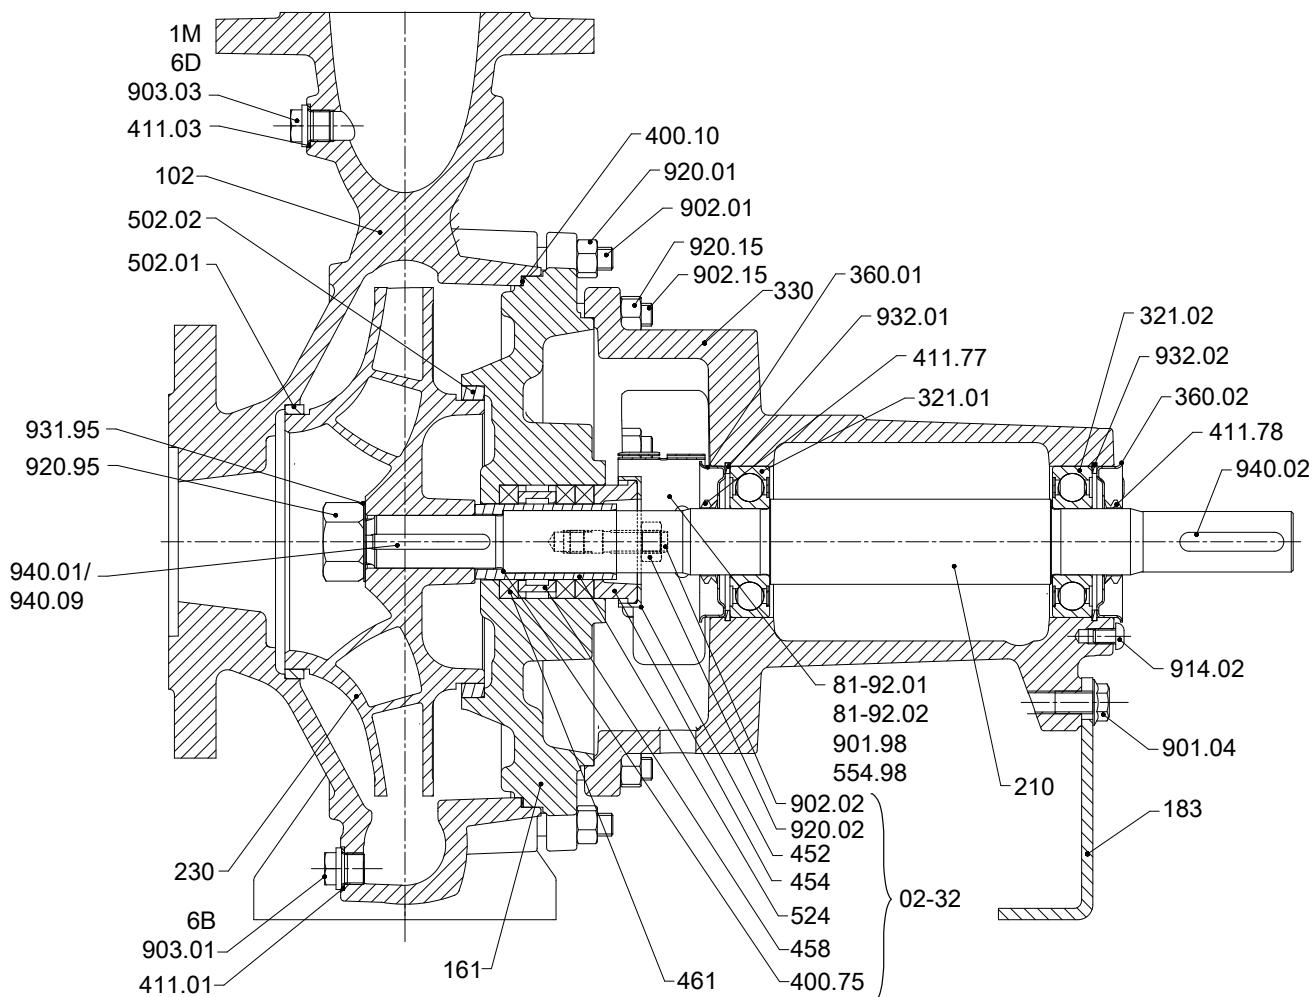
Сборочный чертеж с сальниковым уплотнением, тип Р1 - Na
